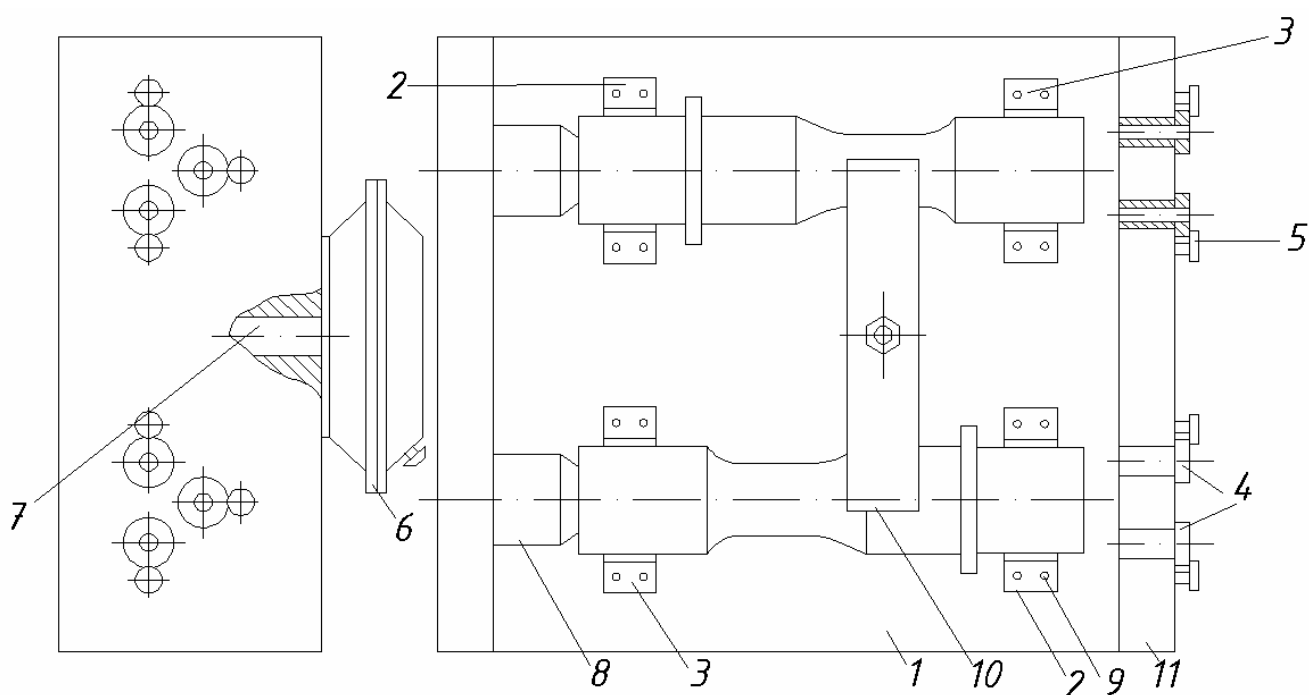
Пристрій для обробки 3-х отв. М10
